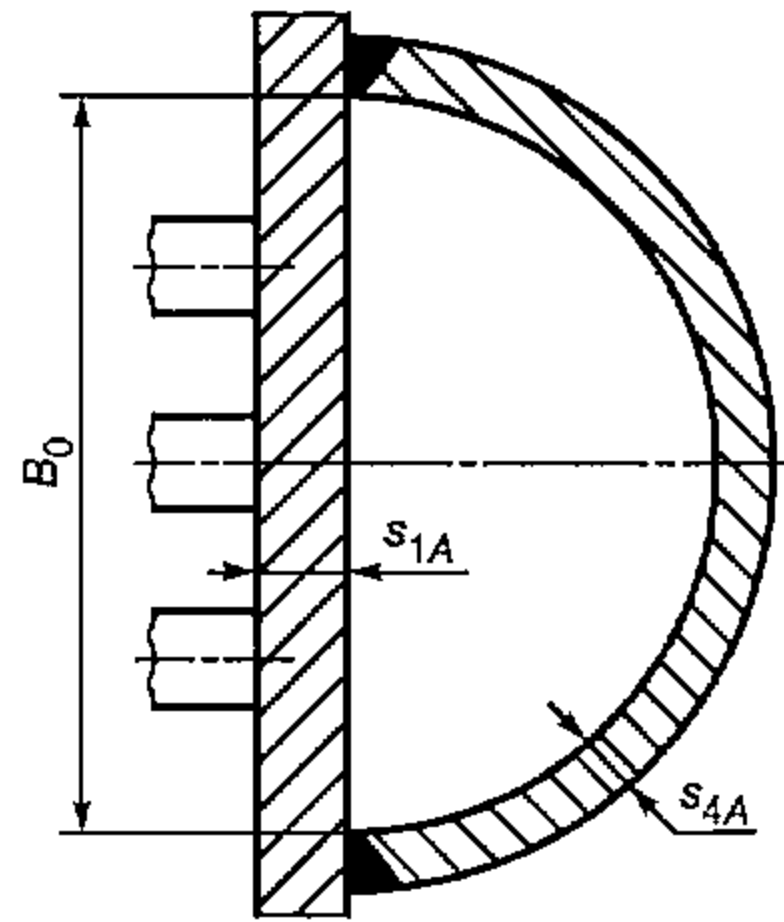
Камера неразъемной конструкции с полуцилиндрической задней стенкой
